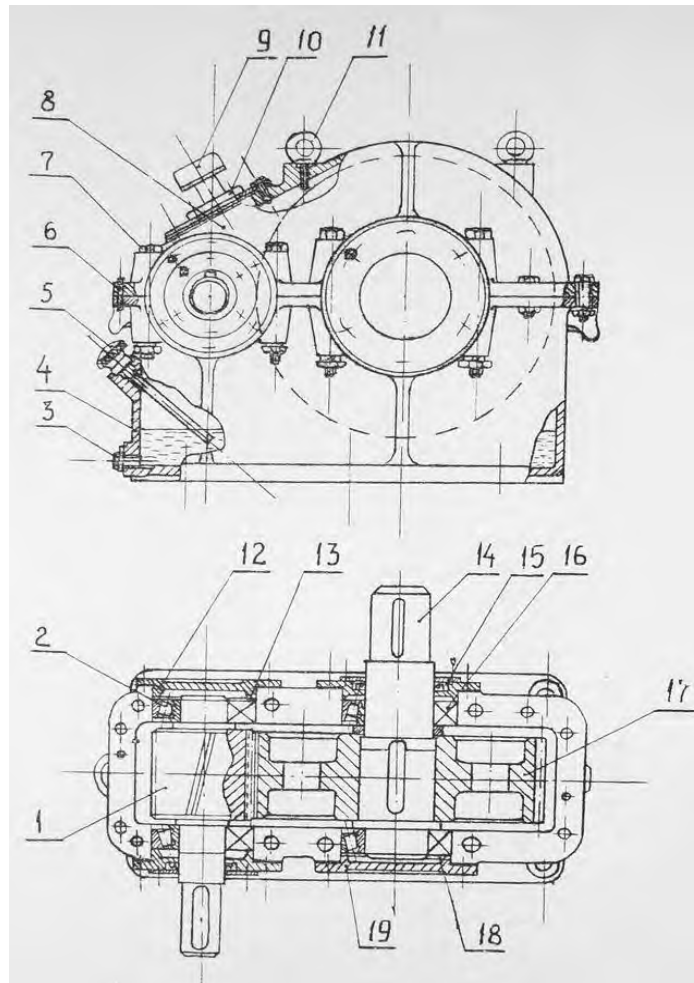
Редуктор зубчатый цилиндрический
